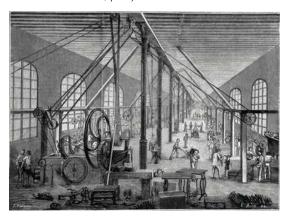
Fábrica de máquinas de coser de Miguel Escuder (IEA, nº. 46 de 15-12-1874, p.12)
